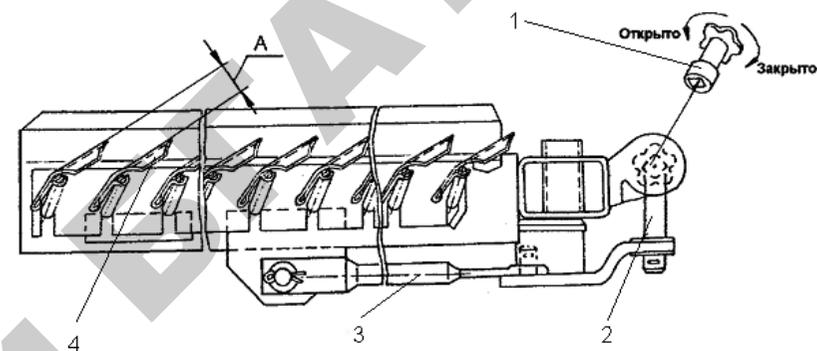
Регулировка размера открытия жалюзи решет: 1 — трубчатый регулировочный ключ с воротком; 2 — механизм регулировки; 3 — тяга; 4 — жалюзи решет; А — зазор положения жалюзи решет
